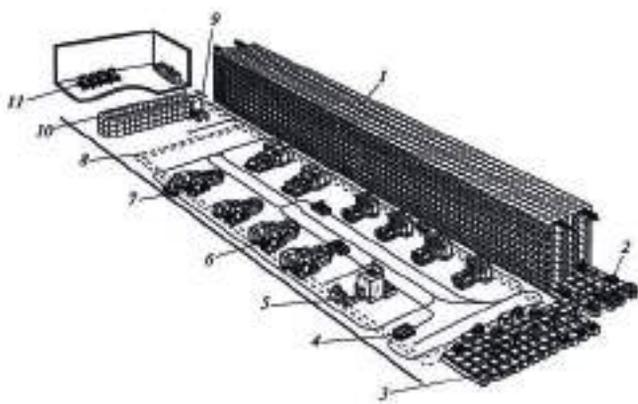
Общий вид ГПС на базе обрабатывающих центров с центральным складом, обеспечивающих гибкость производства: 1 – склад заготовок; 2 – конвейер; 3 – зона установки заготовок на паллеты; 4, 7 – транспортные тележки-робокары; 5 – станция мойки; 6 – ОЦ; 8 – транспортёр; 9 – оборудование настройки инструмента; 10 – склад инструментов; 11 – центр управления ГПС
